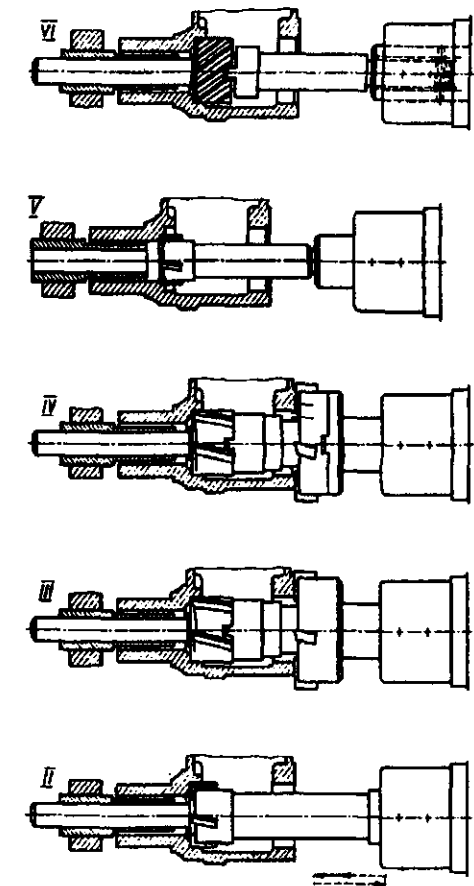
Схемы обработки корпусной детали: I – снять и закрепить заготовку (не показано); II – зенкеровать два отверстия диаметром 68 мм "в линию"; III – зенкеровать два отверстия диаметром 70 мм "в линию" и предварительно подрезать наружный торец; IV – зенкеровать два отверстия диаметром 71,5 мм "в линию", снять фаску и окончательно подрезать наружный торец; V – снять фаску; VI – развернуть два отверстия диаметром $72^{+0,03}$ мм "в линию"
